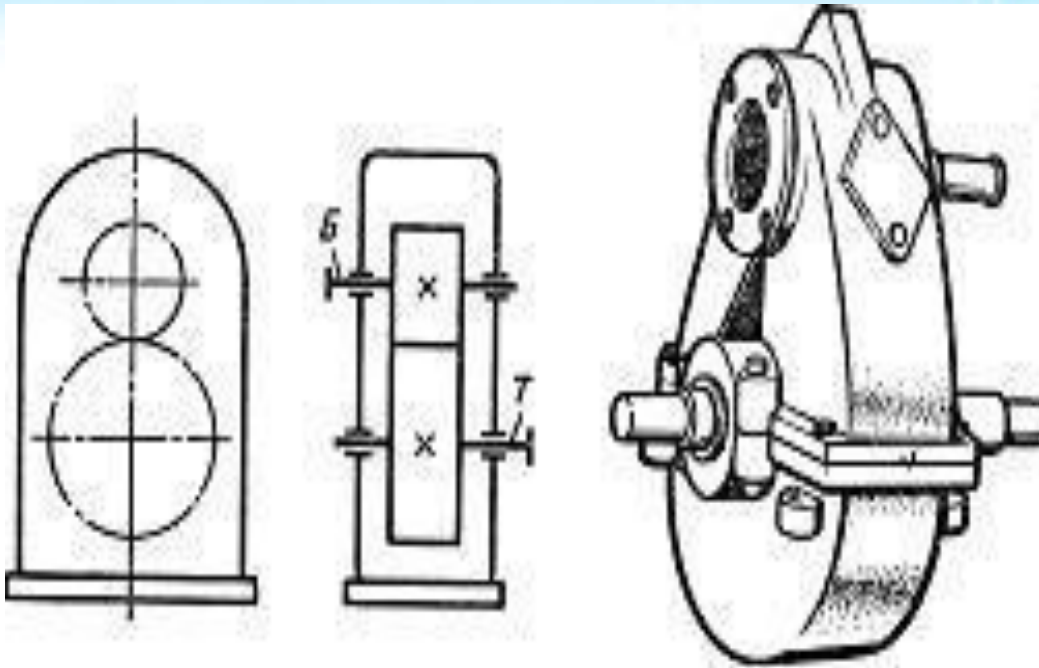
Одноступенчатый цилиндрический редуктор вертикальный
